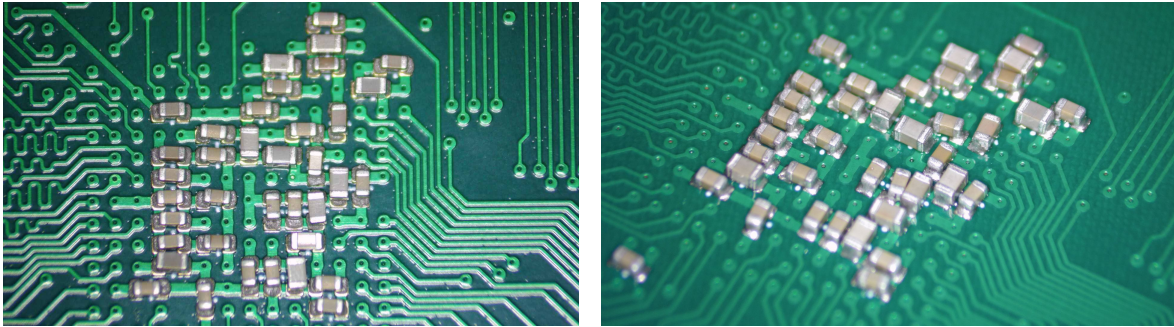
Soldadura de los componentes de la cara inferior.
